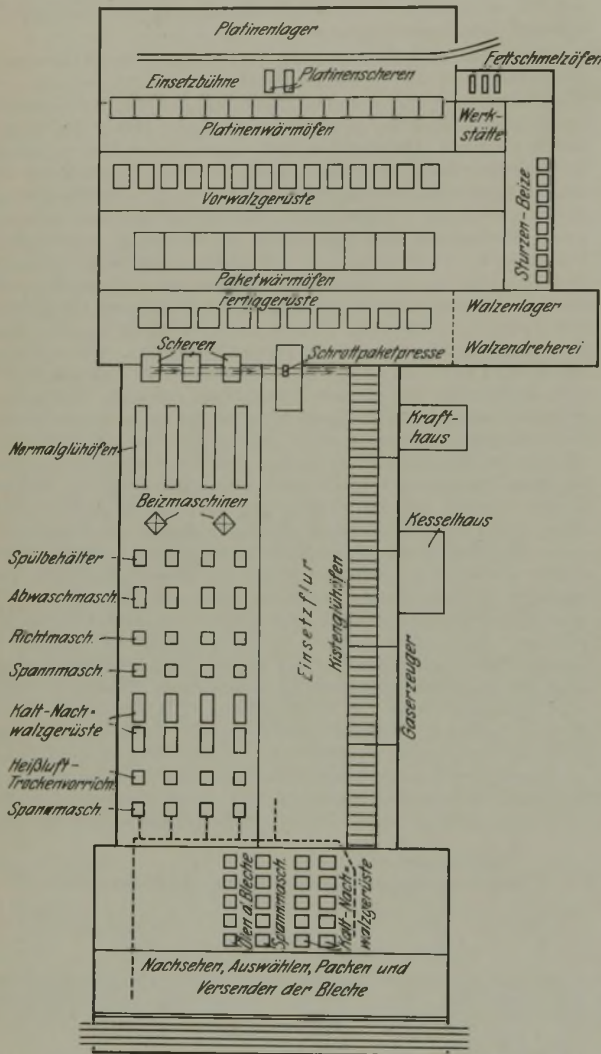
Grundriß des Feinblech-Walzwerkes der Newton Steel Co.
